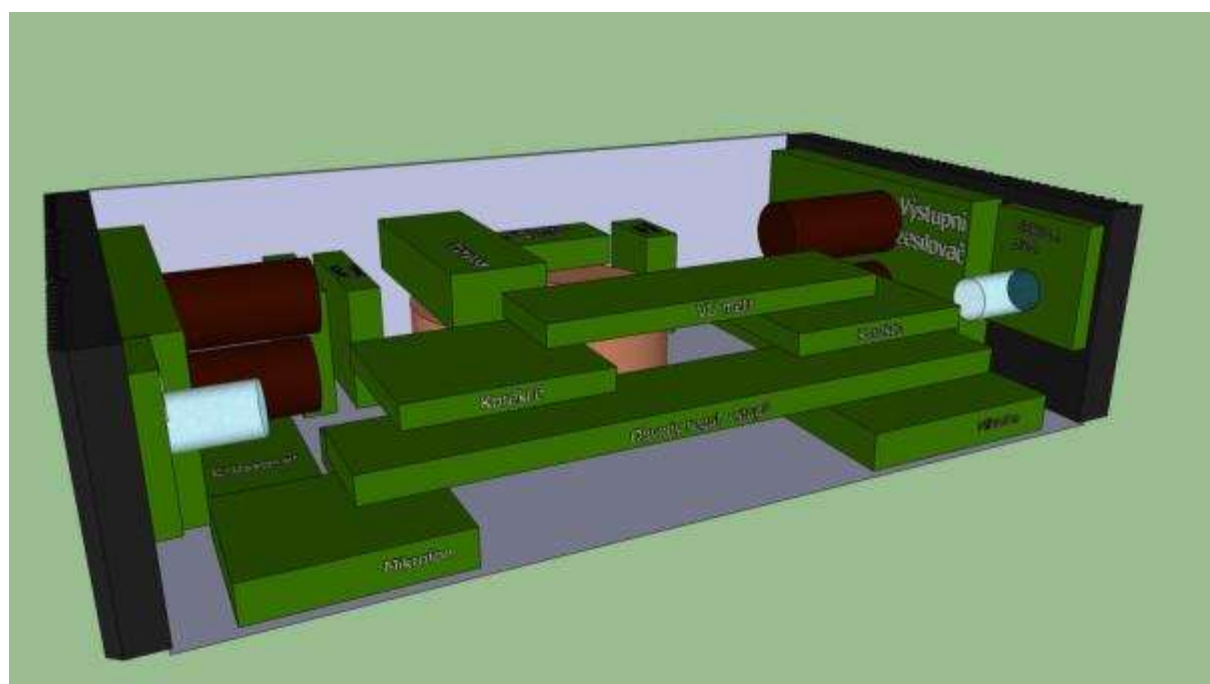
Rozmístění desek plošných spojů ve skříni: boční pohled
